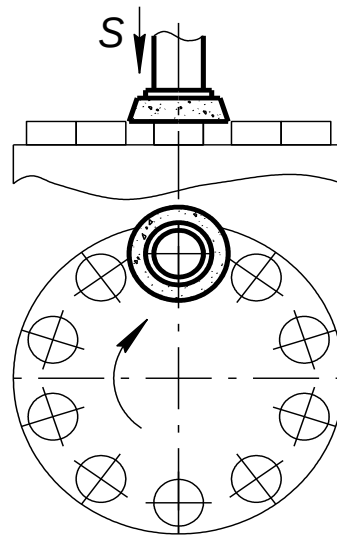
Багатомісна паралельно-послідовна обробка з одночасною установкою заготовок
